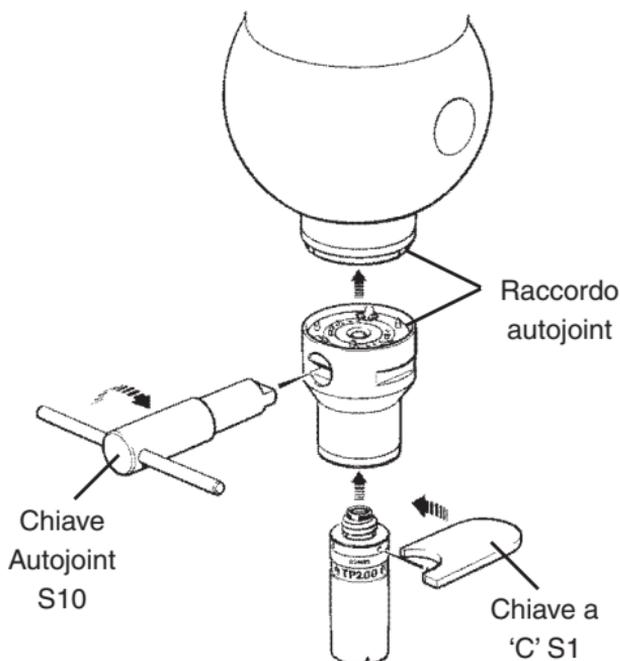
Montaggio del sensore TP200 su testina con Autojoint
